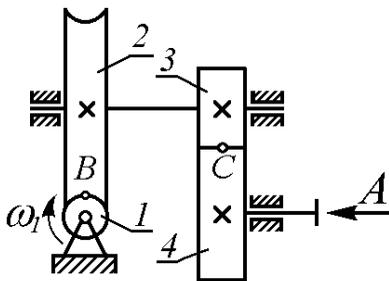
Двоступінчастий черв'ячно-циліндричний редуктор
